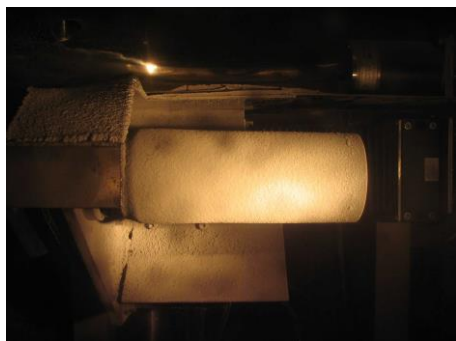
Цилиндрическая заготовка, полученная методом *Spray forming
